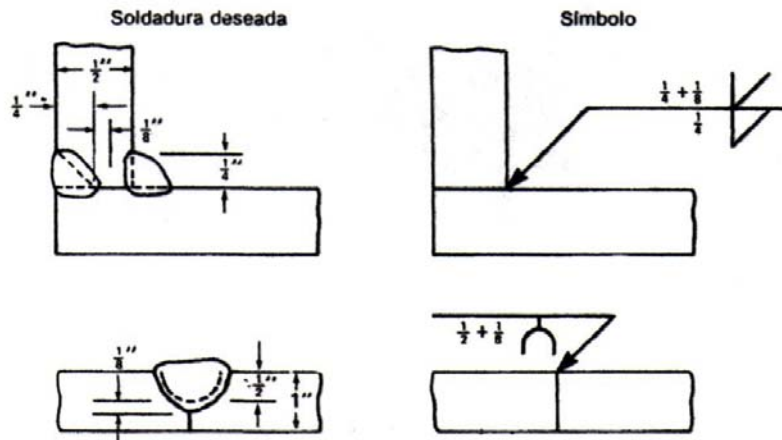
Símbolos de soldadura en los que se especifica la profundidad de las ranuras y la profundidad de penetración
